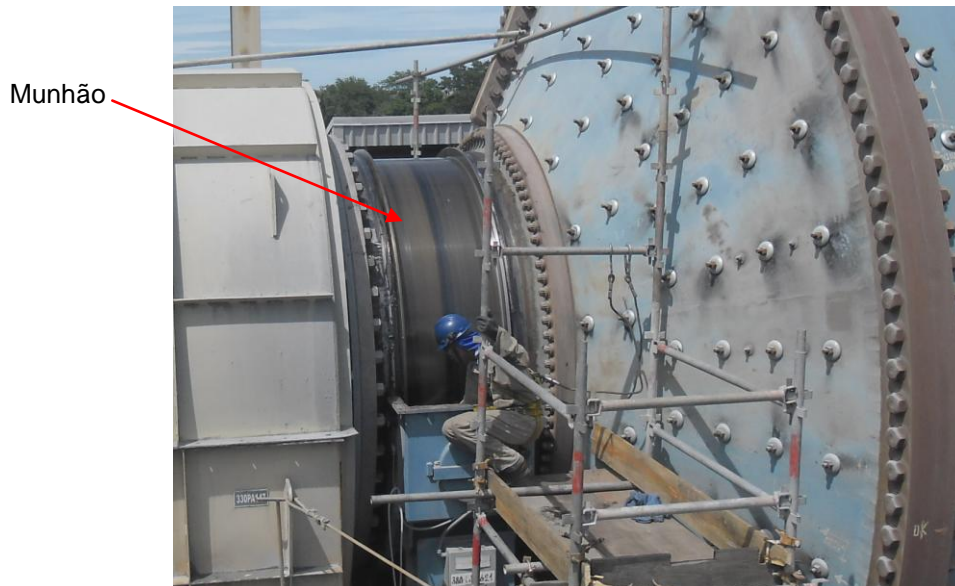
Detalhe da plataforma posicionada ao lado do munhão para permitir acesso aos operadores para inspeção
